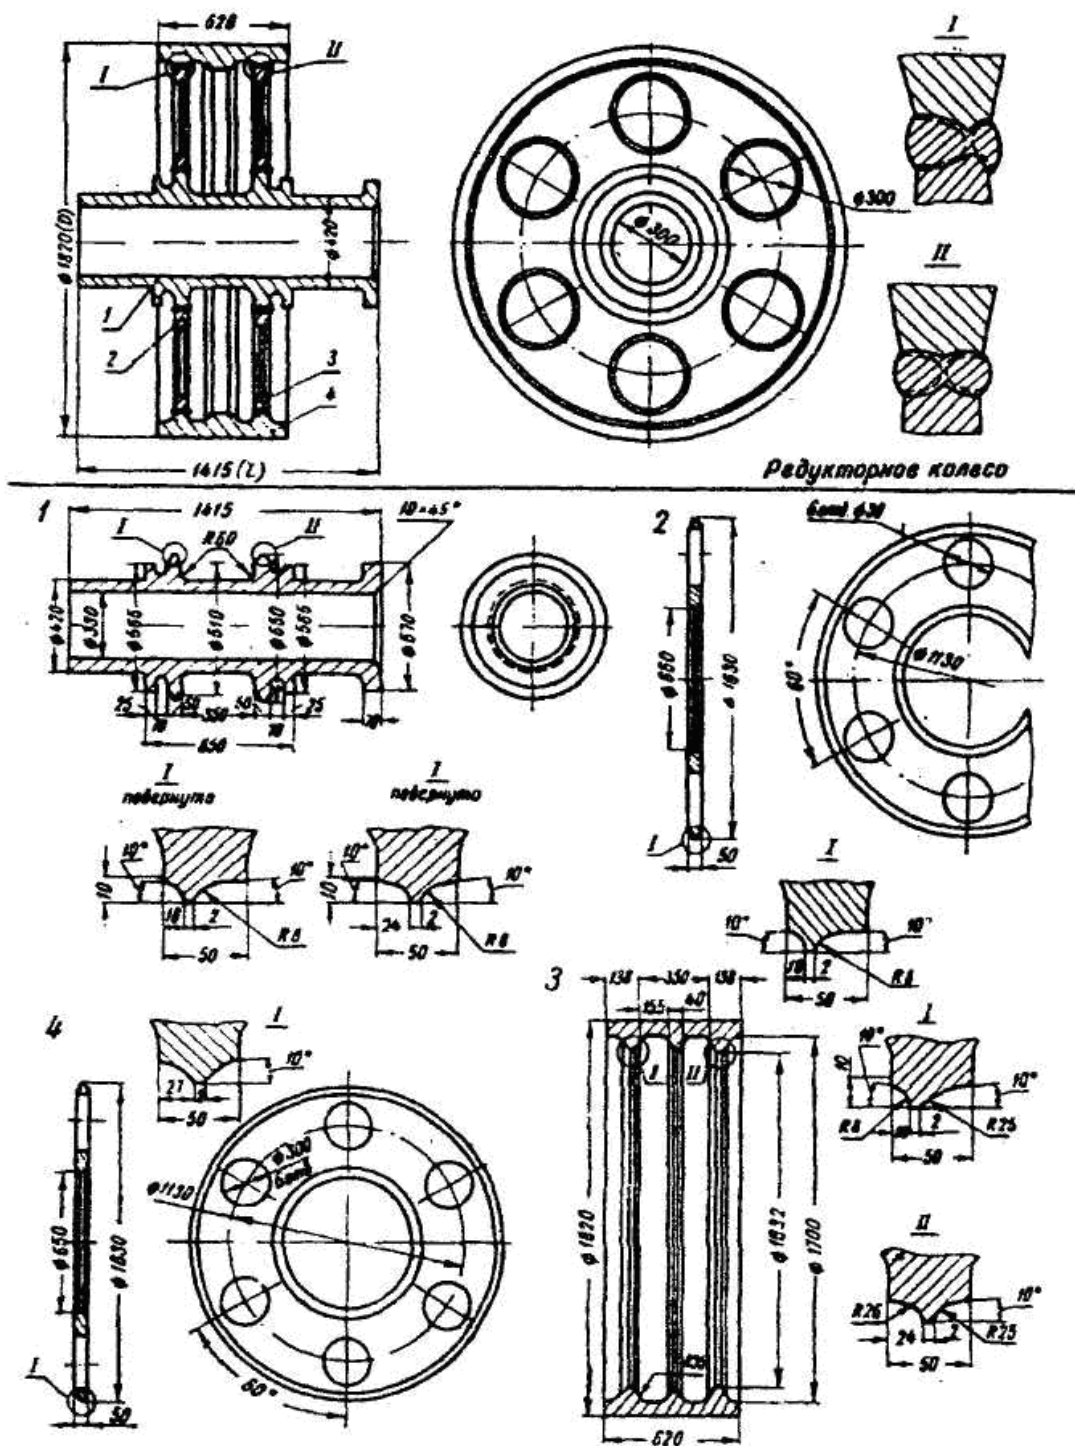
Эскизы редукторного колеса и его деталей для задания № 8
